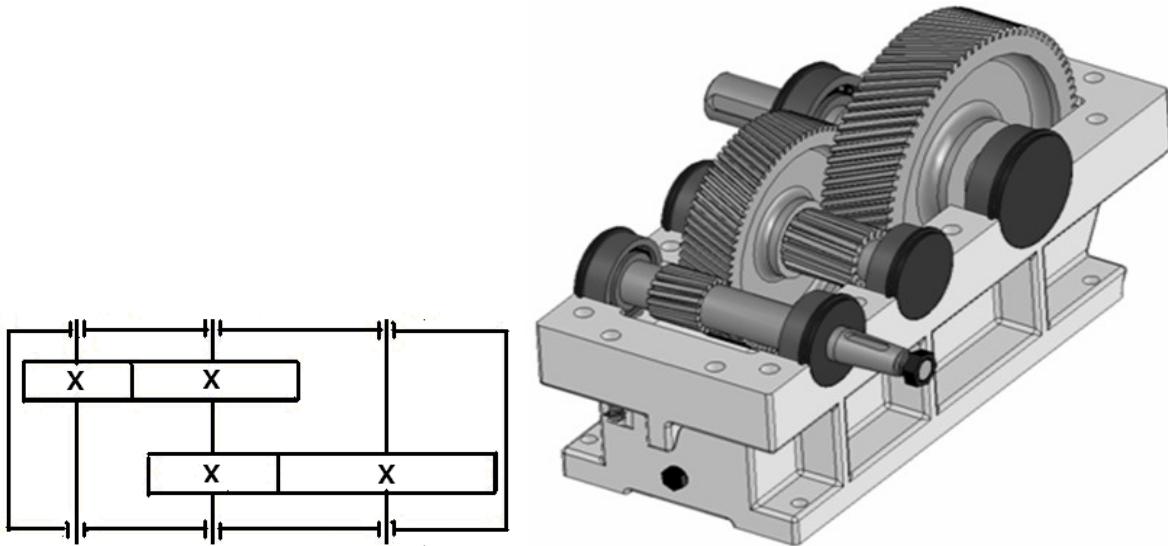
Цилиндрический двухступенчатый редуктор с последовательным расположением ступеней
